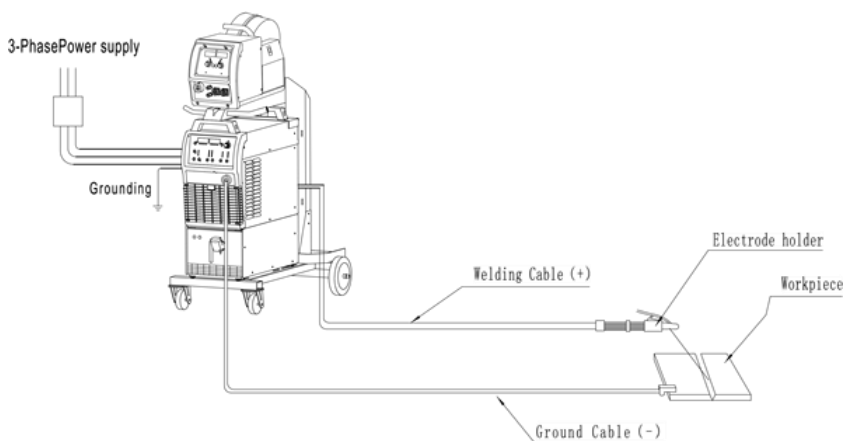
Комплект для ручной дуговой сварки
